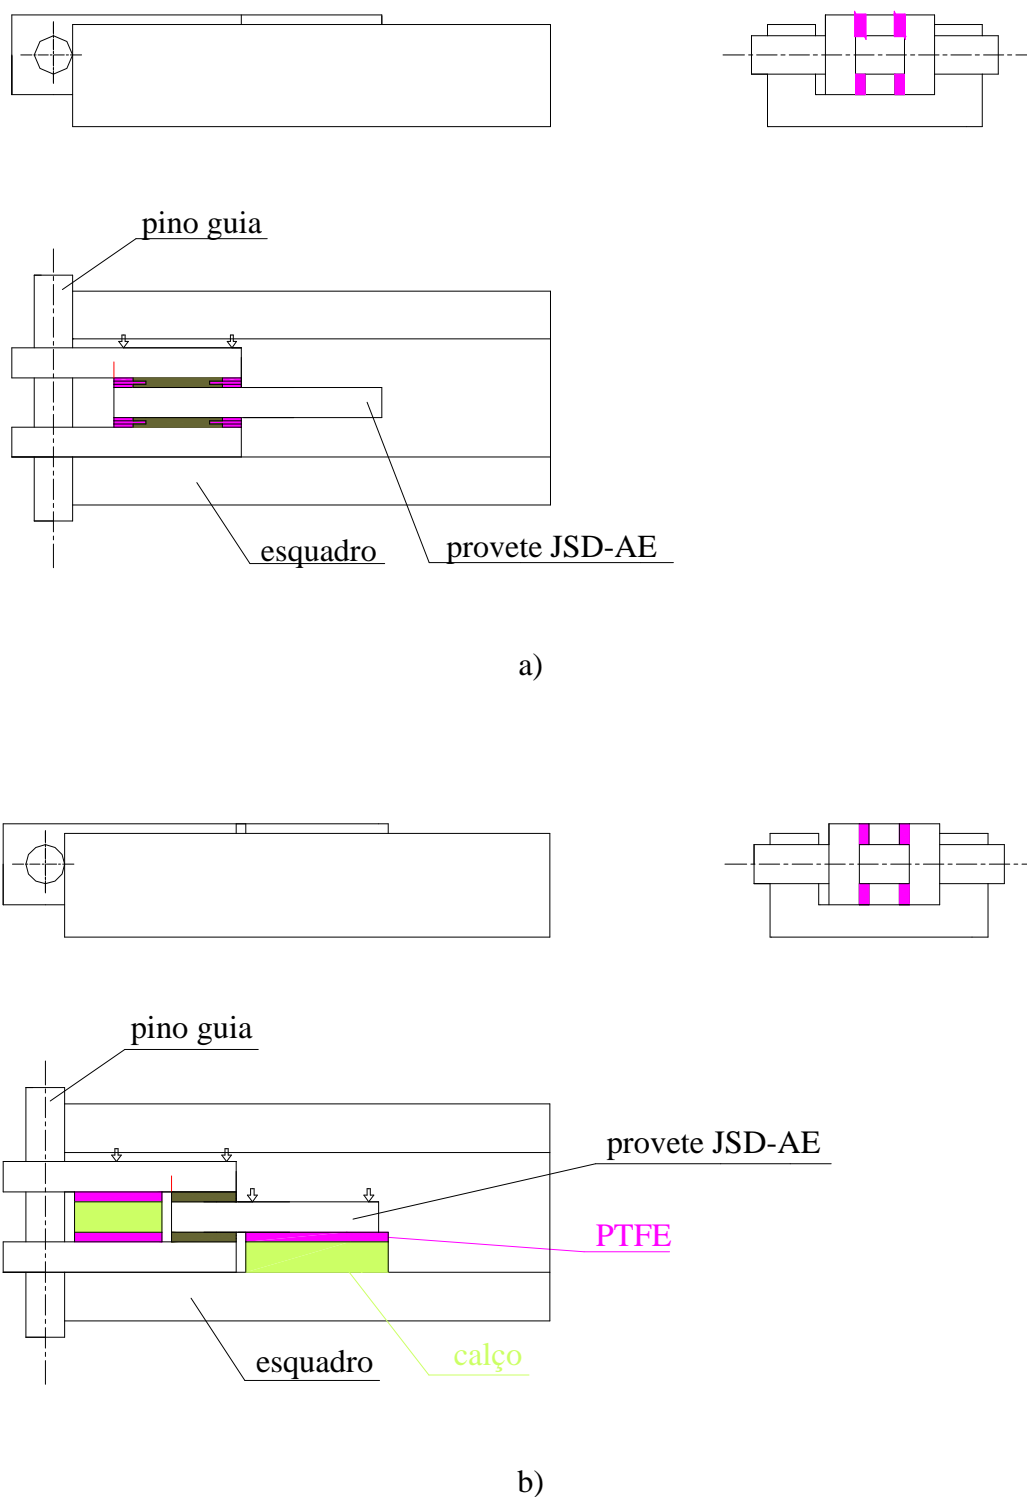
Preparação do provete JSD-AE para ensaios de tracção: a) com fendas de 10 mm; b) sem fendas.
